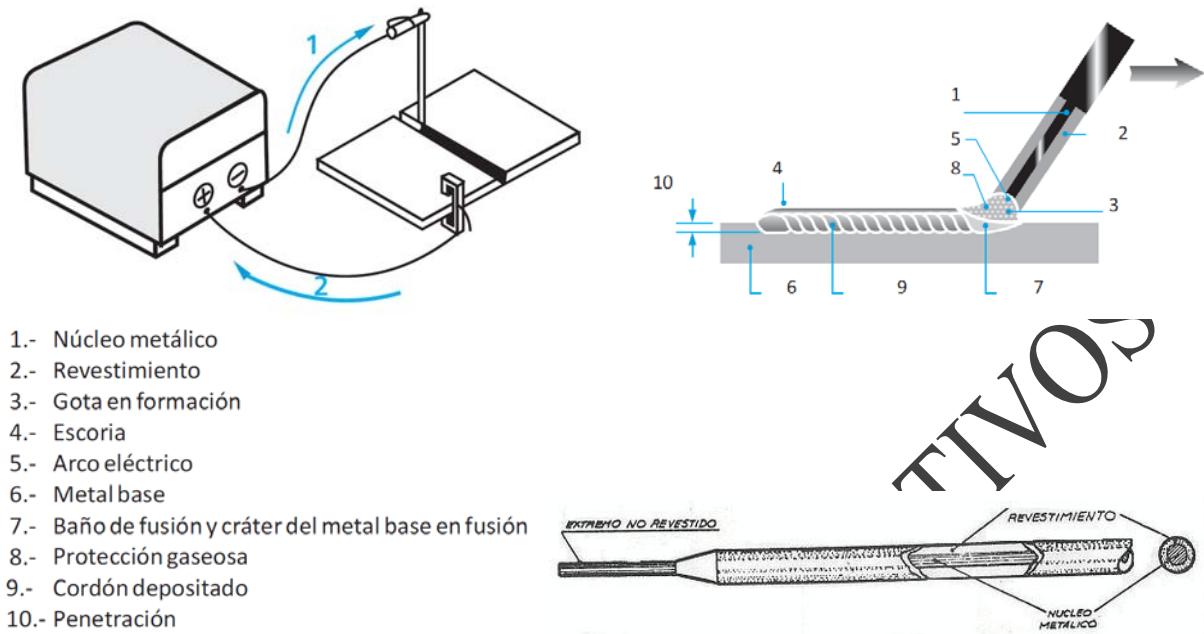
Proceso de soldadura por arco con electrodo revestido
